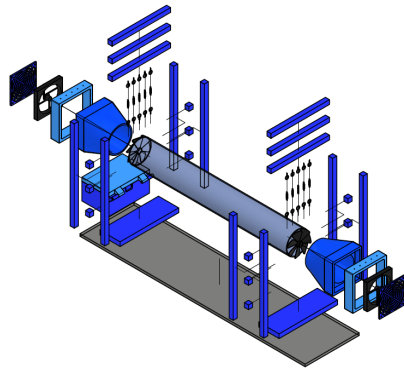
Vista explosionada del modelo CAD del dispositivo experimental.
